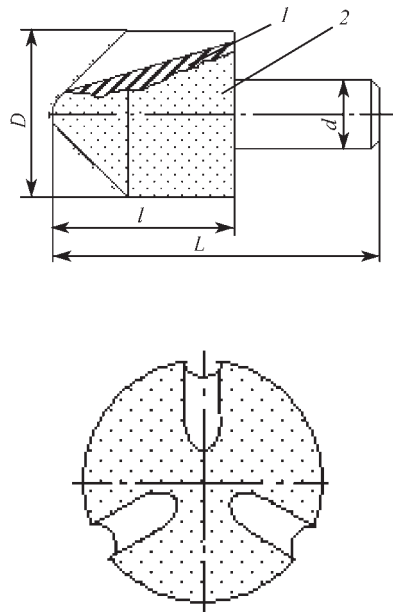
Конструкция алмазно-абразивного стержневого сверла:
